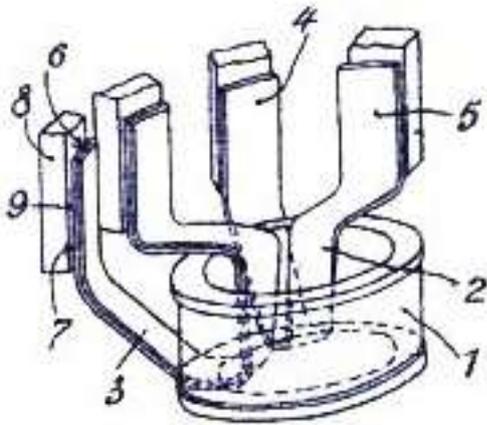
Stabilisierungsrings zur Fixierung der Pollücken
